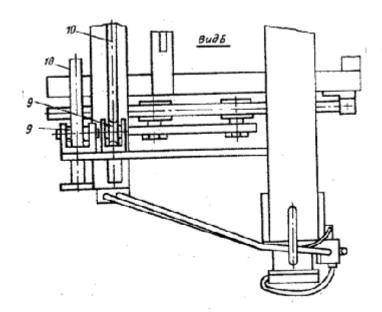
Вид Б стенда для разборки и сборки коробок передач «Стенд работает следующим образом» [12].
